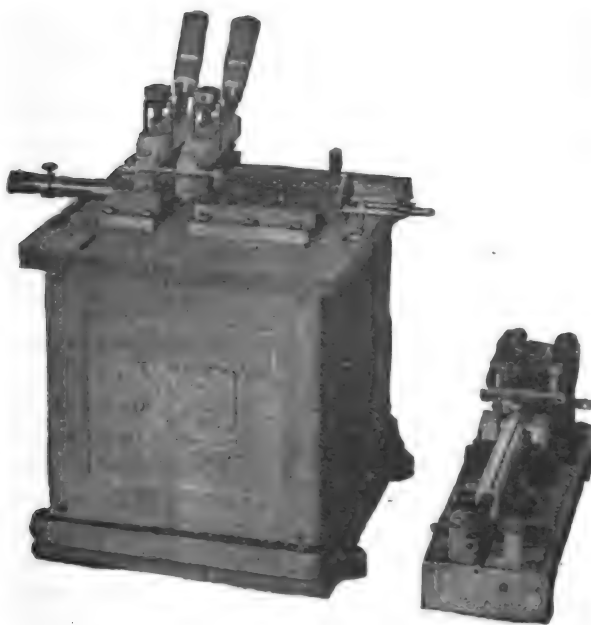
Machine à souder et interrupteur automatique de courant.
